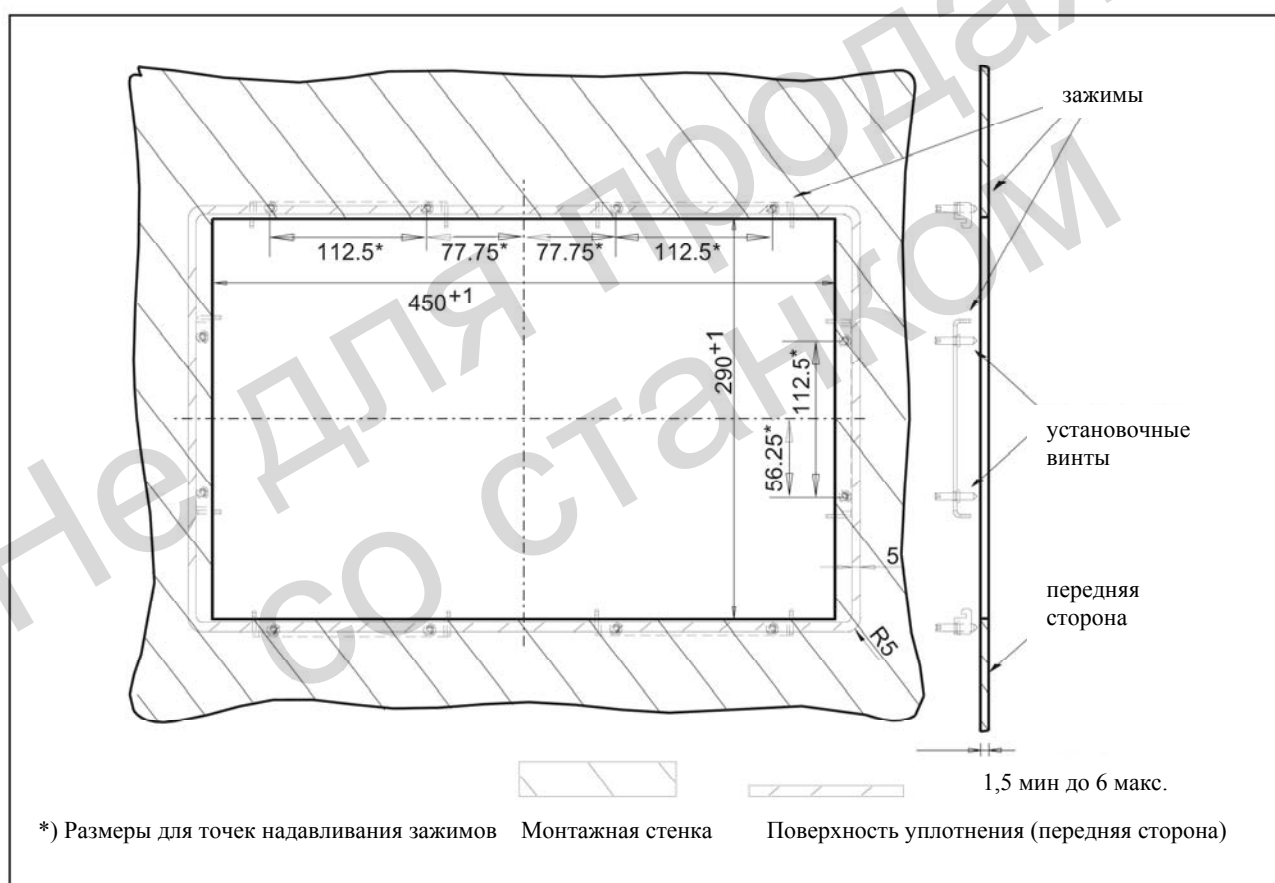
Габаритный чертеж для монтажа панели оператора OP 010C
